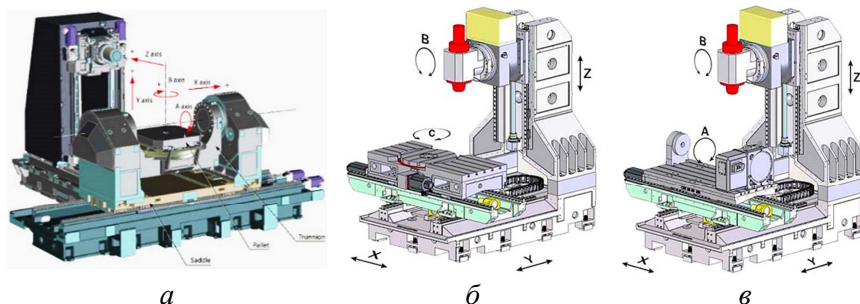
5-осевые фрезерно-сверлильно-расточные станки с ЧПУ:
